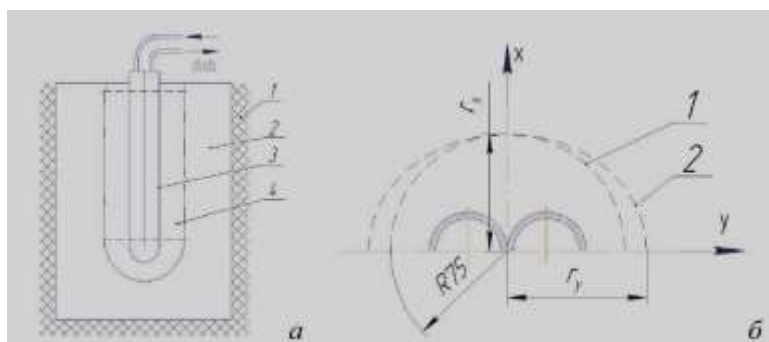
Схема намораживания (а) и форма намороженного слитка (б): 1 – контур желаемой заготовки; 2 – контур получаемой заготовки
